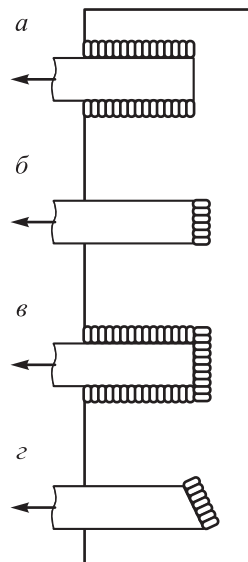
Виды сварных швов по отношению к направлению действующих усилий: *а* — фланговый; *б* — лобовой; *в* — комбинированный; *г* — косой
